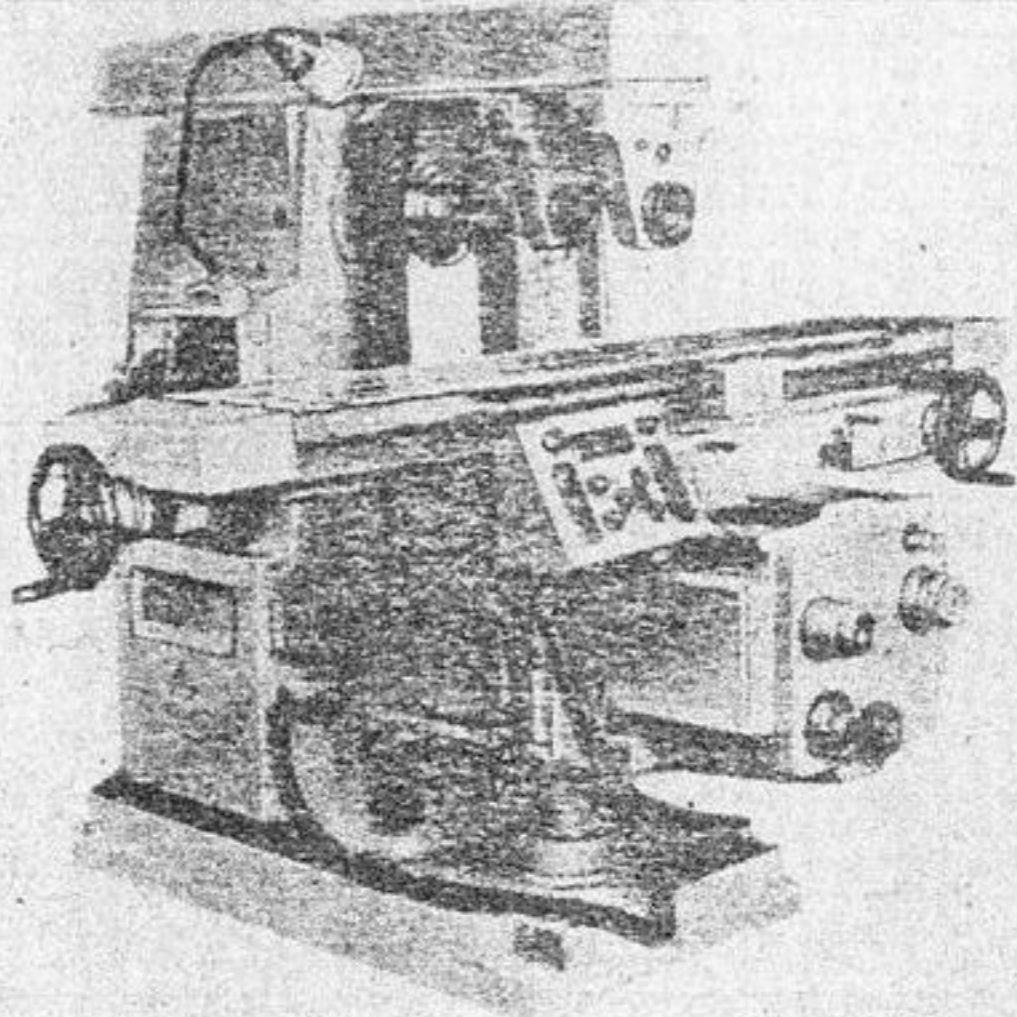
Горизонтальный консольно-фрезерный станок 6Т83Г-29
